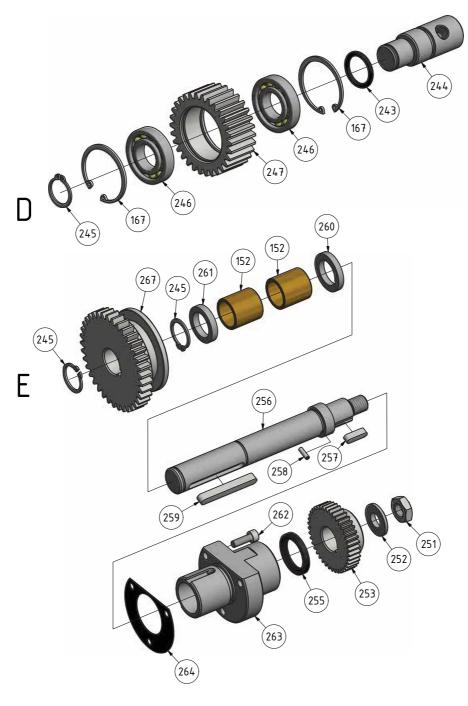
Getriebe Spindelstock 5-6 - Headstock gear 5-6
